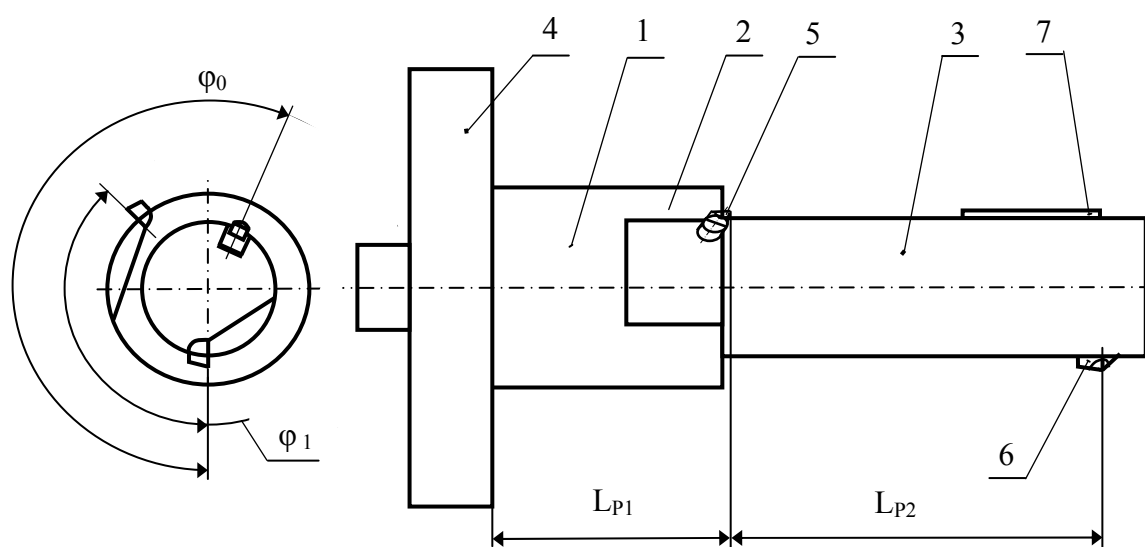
Комбинированный расточный инструмент с виброзащитным направляющим элементом для обработки ступенчатого отверстия: 1 – корпус, 2 и 3 – первая и вторая ступень расточного инструмента, 4 – фланцевая часть корпуса для крепления к шпинделю отделочно-расточной головки, 5 и 6 – режущие элементы первой и второй ступени, 7 – ограниченно подвижный упругий направляющий элемент второй ступени.
